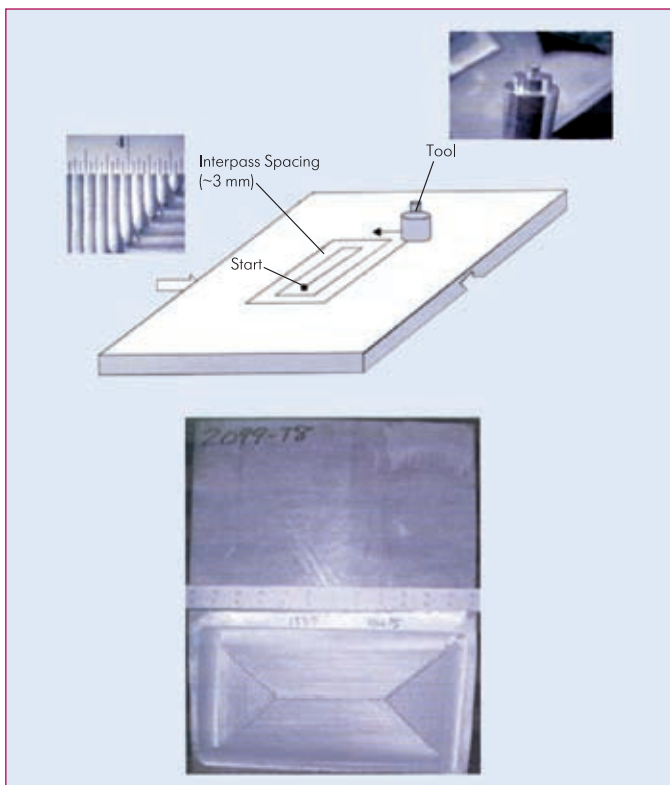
Схема и общий вид пластины до и после обработки FSP-методом
